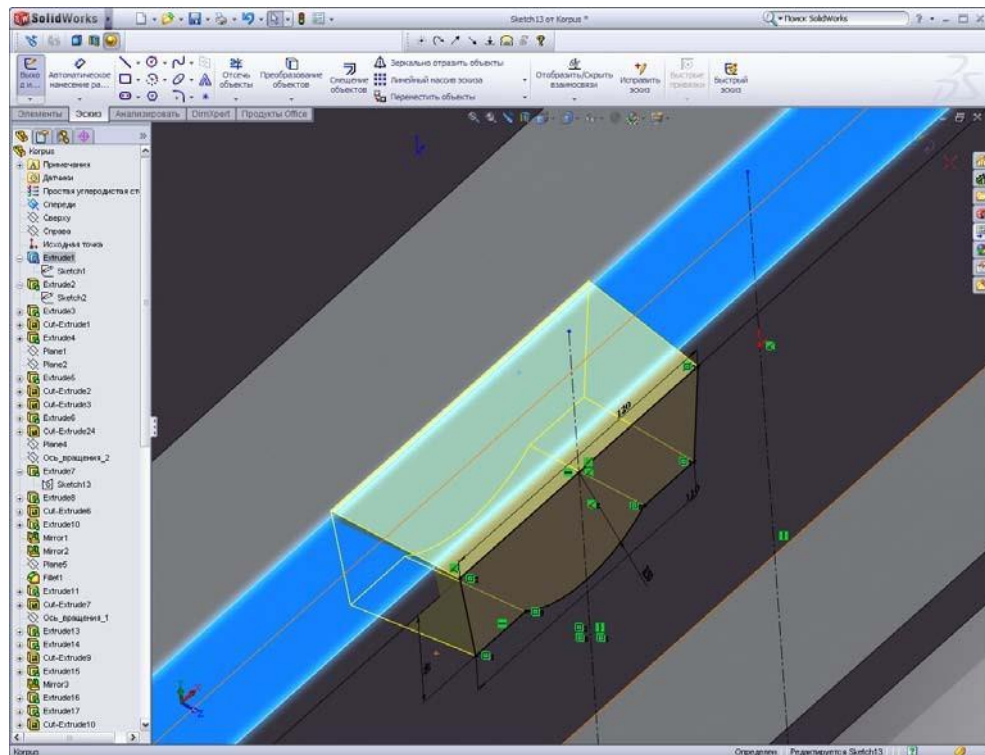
Редагування ескізу бобишки на площині стінки деталі корпуса
